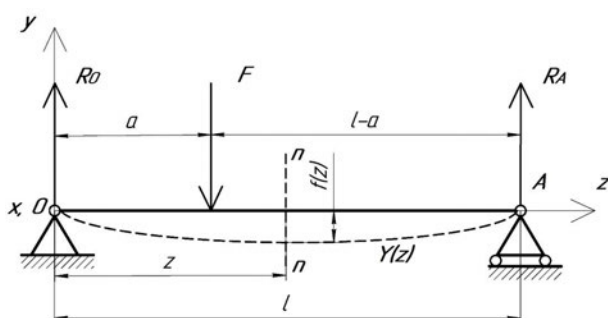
Схема силового расчета изгиба листовой металлической заготовки
